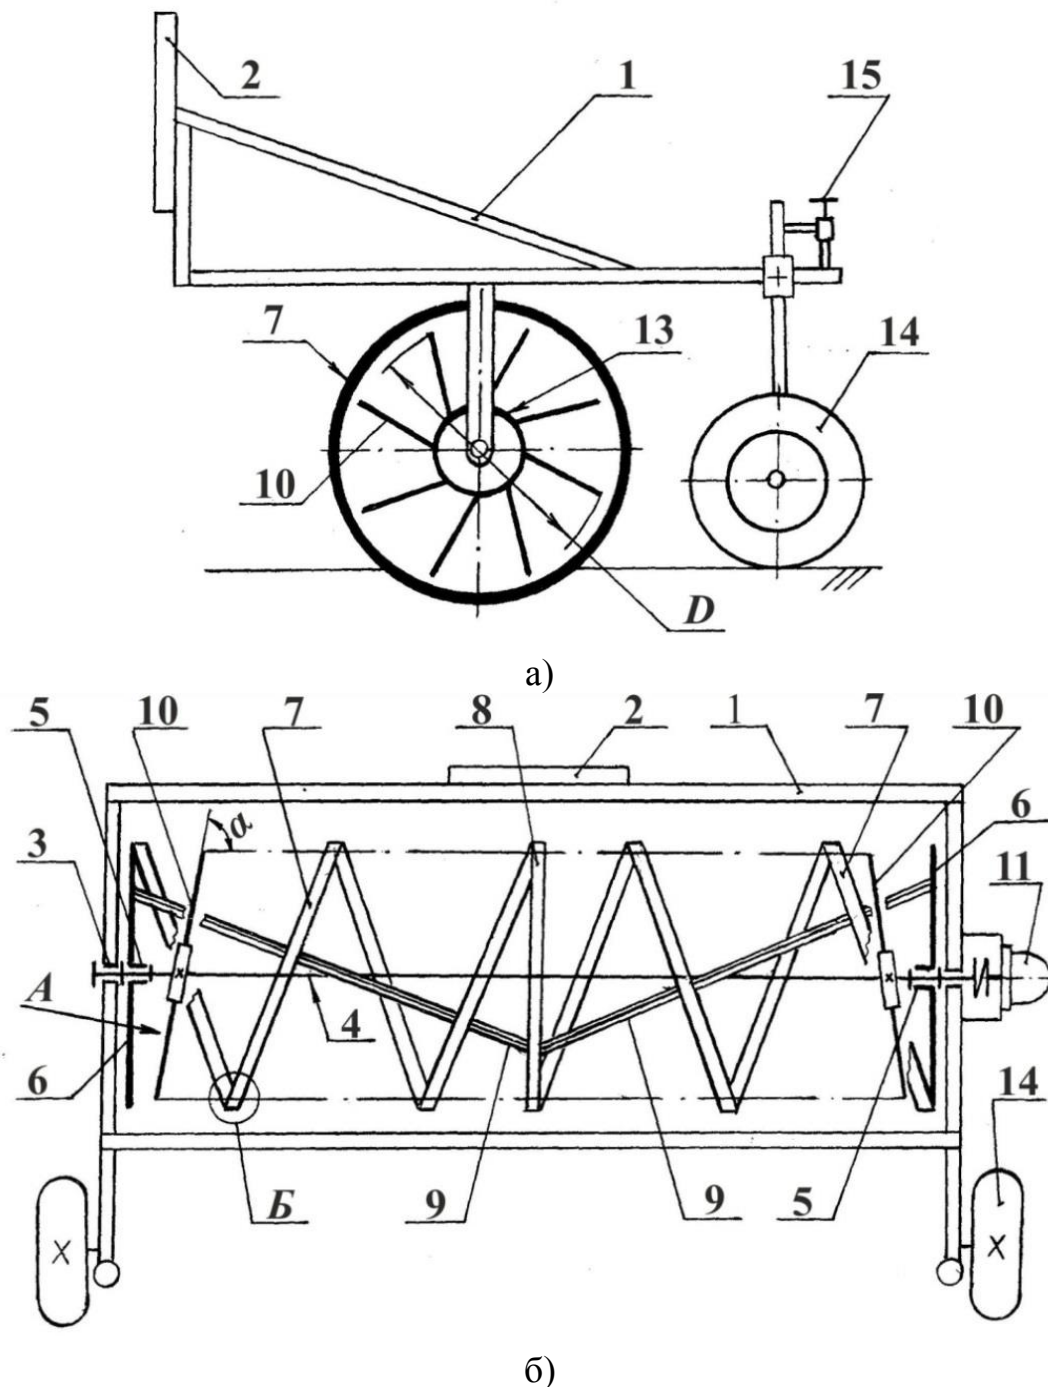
Конструктивно-технологічна схема ротaційного знаряддя (а - робоче положення; б - вигляд зверху): 1 – рама; 2 – механізм навішування; 3 і 5 – підшипникові опори; 4 – вал; 6 – круглі бічні диски; 7 – стрічкові спіралі; 8 – з'єднувальне кільце; 9 – гвинтові квадратні прутки; 10 – еліпсоподібні голчасті диски; 11 – гідромотор; 12 – голка диска; 13 – маточина диска; 14 – опорні колеса; 15 – гвинтовий механізм регулювання глибини обробки.
